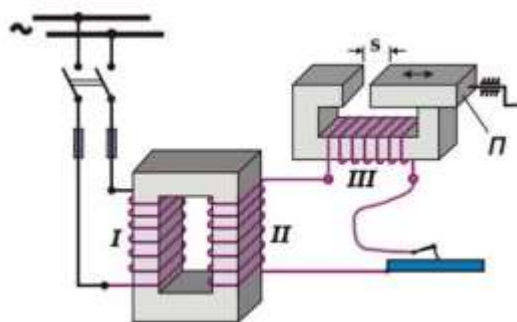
Схема сварочного трансформатора типа СТЭ 34
